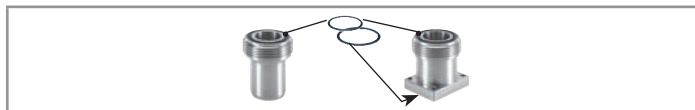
Уплотнительное кольцо для переходника из нержавеющей стали
